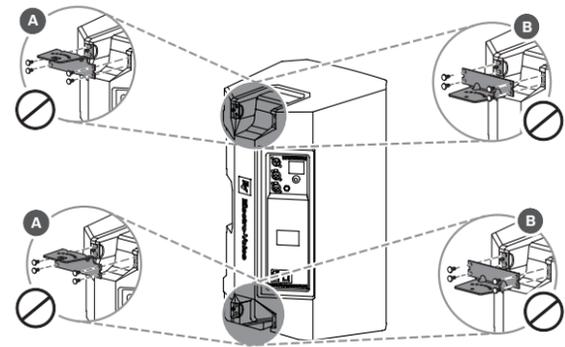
Instalação incorreta da placa de montagem superior e inferior em versões de 12 polegadas
